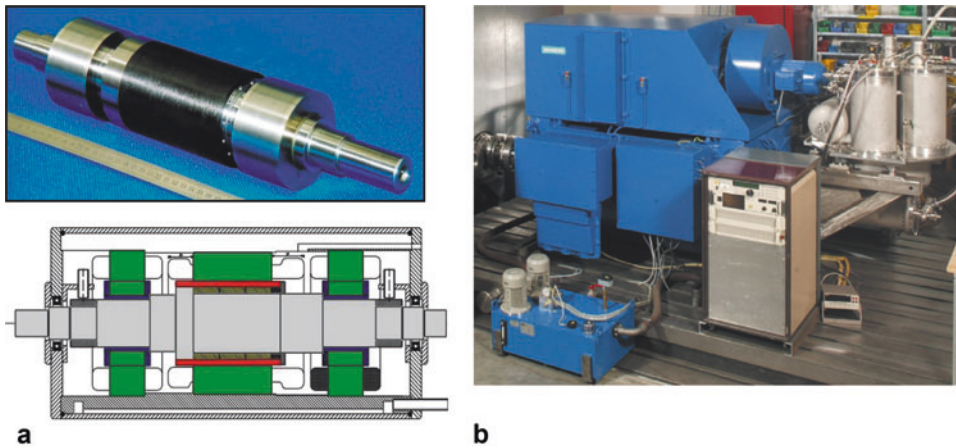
(a) Magnetgelagerter 40 kW-Permanentmagnet-Synchronmotor mit Kohlefaserbandage zur Läufermagnetbefestigung bei 40000/min als Kompressorantrieb, oben: PM-Läufer mit zwei Radialmagnetlagern, unten: axialer Schnitt durch den Motor (Mitte) und die beiden Radialmagnetlager (links und rechts) (Quelle: Klohr 2007), (b) Zweipoliger 4 MW-Synchrongenerator für Schiffe, 3600/min, 60 Hz, Hochtemperatur-Supraleiterwicklung im Läufer, Neon-Kaltgaskühlung, 30 K (Quelle: Siemens AG)
